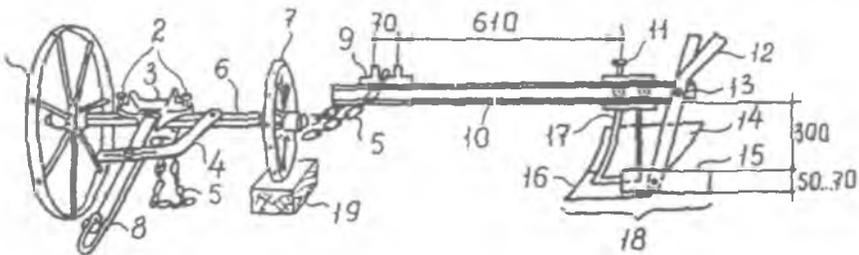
Плуг с простым (нерегулируемым) передком: 1 - правое, бороздное колесо; 2 - регулировочные болты; 3 - подушка; 4 - изогнутая планка; 5 - цепь; 6 - цепельная ось; 7 - левое полевое колесо; 8 - упряжный крюк (тяги); 9 - крючок (упор) для цепи; 10 - грядиль; 11 - болт для регулировки поворота корпуса; 12 - рукоятки; 13 - регулировочный болт; 14 - отвал; 15 - полевая доска; 16 - лемех; 17 - стойка корпуса (высокая); 18 - корпус плуга; 19 - подставка
